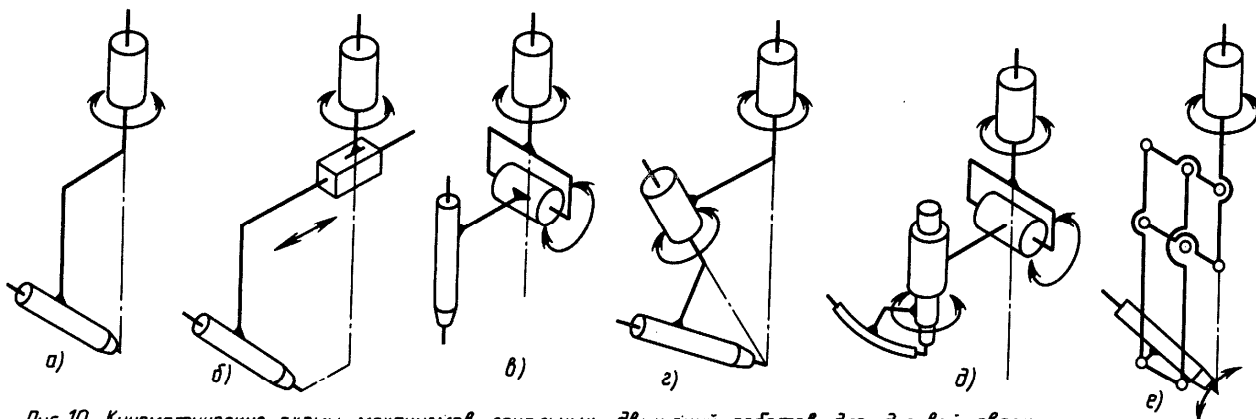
Кинематические схемы механизмов локальных движений роботов для дуговой сварки
